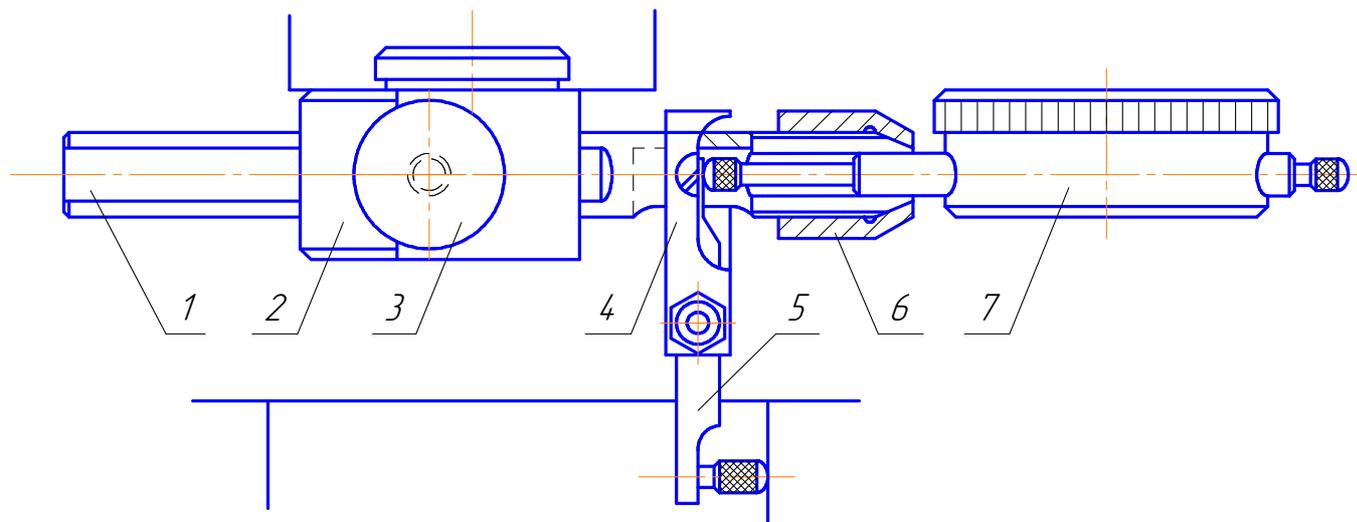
Установка гильзы для расточки по приспособлению с индикатором:
